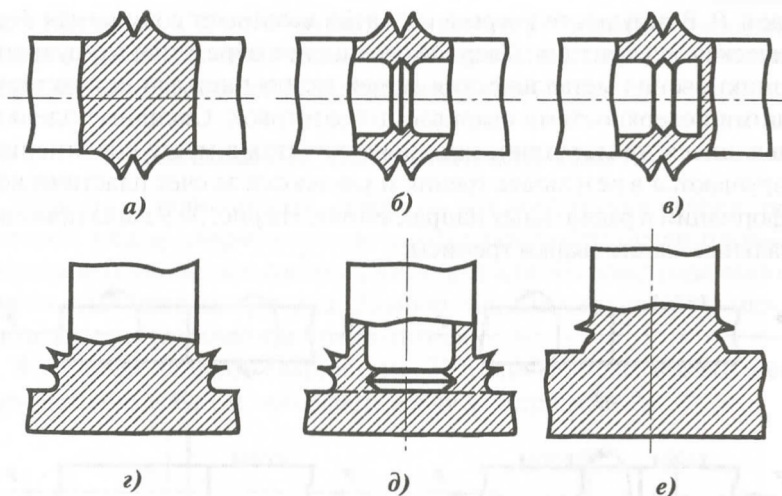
Типы сварных соединений сварки трением:
